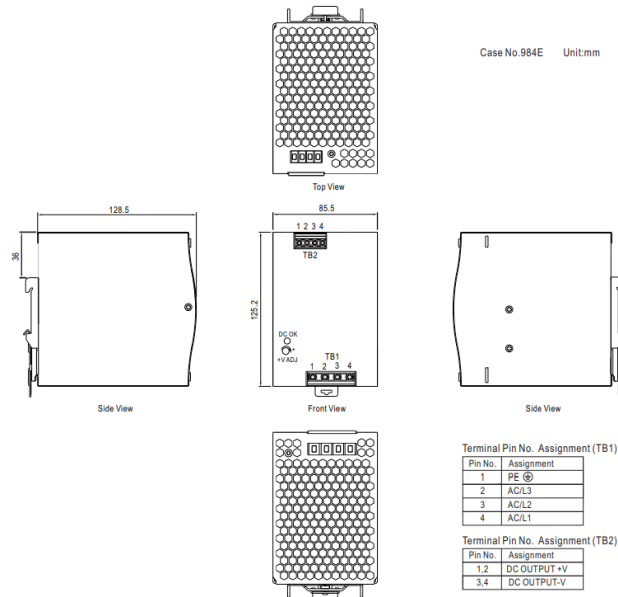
Загальний вигляд габаритів блока живлення
